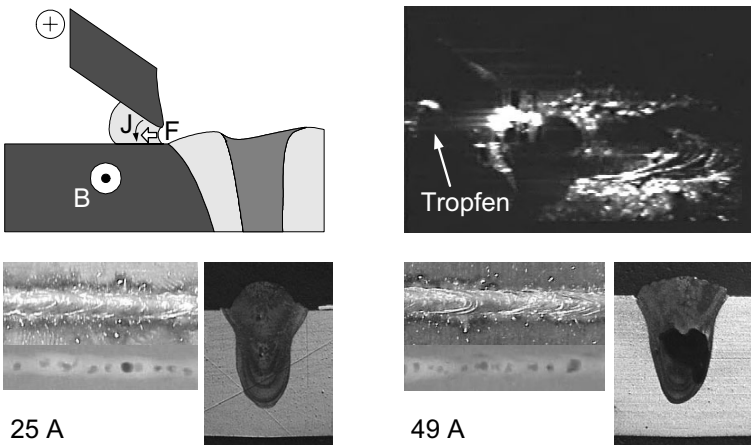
Kraft in Schweißrichtung führt bei AA5182 zur Bildung von Spritzern
